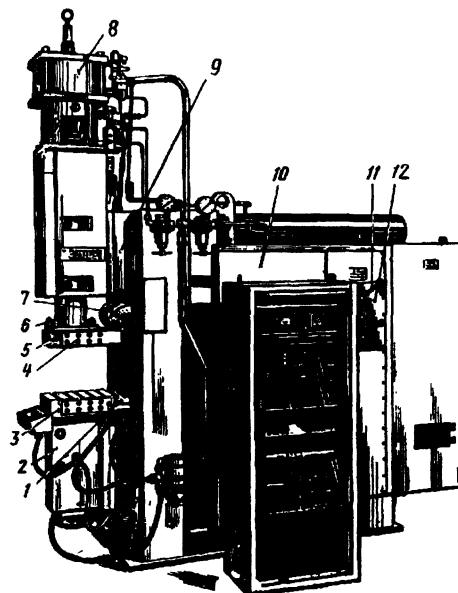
Рельефная машина низкочастотной контактной сварки типа МРН-24001
